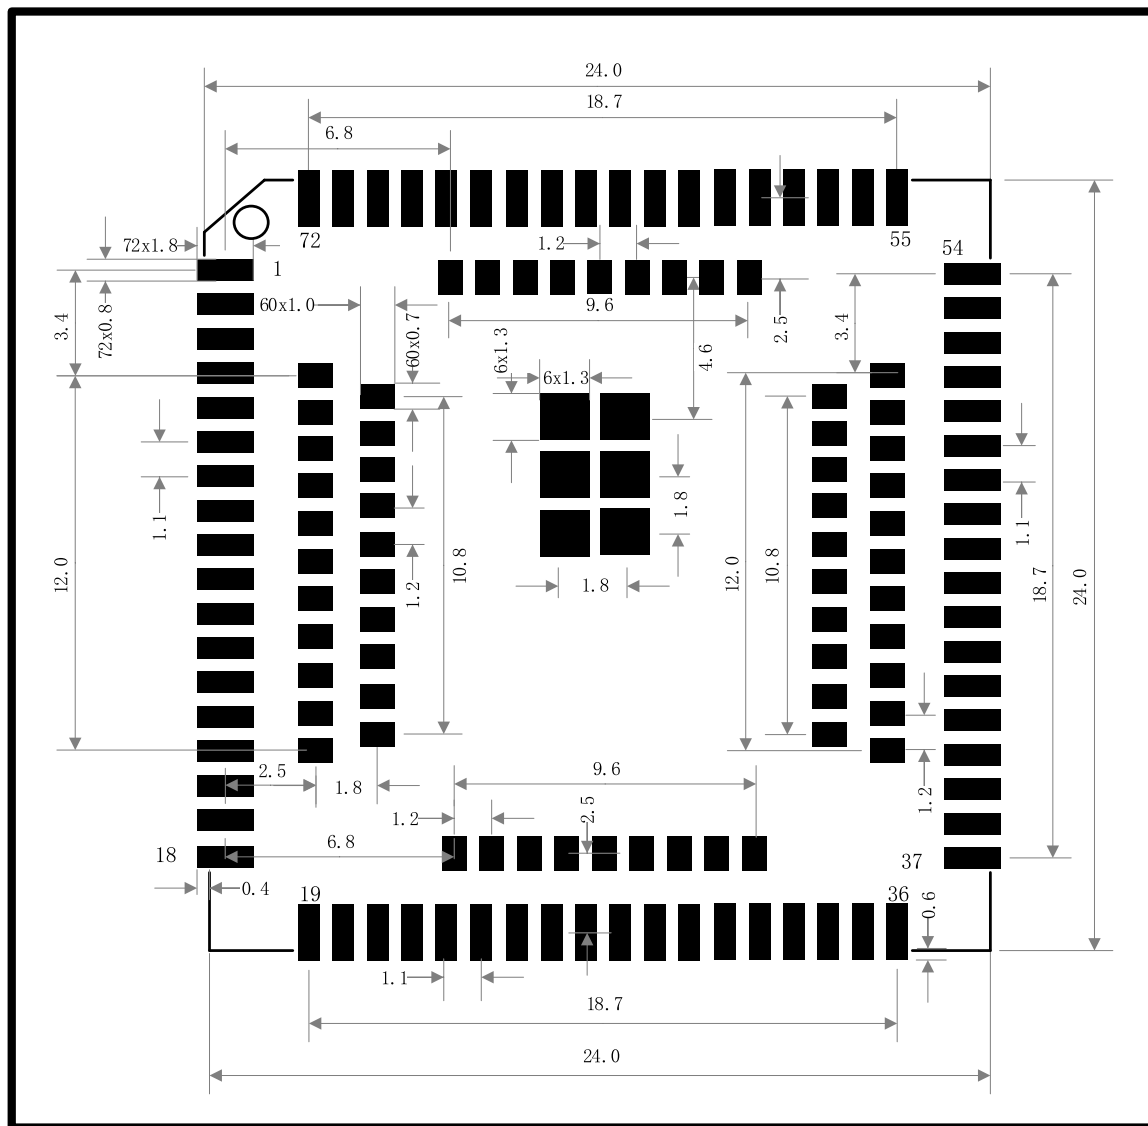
SF32LB58-MOD 推荐 PCB 封装图
